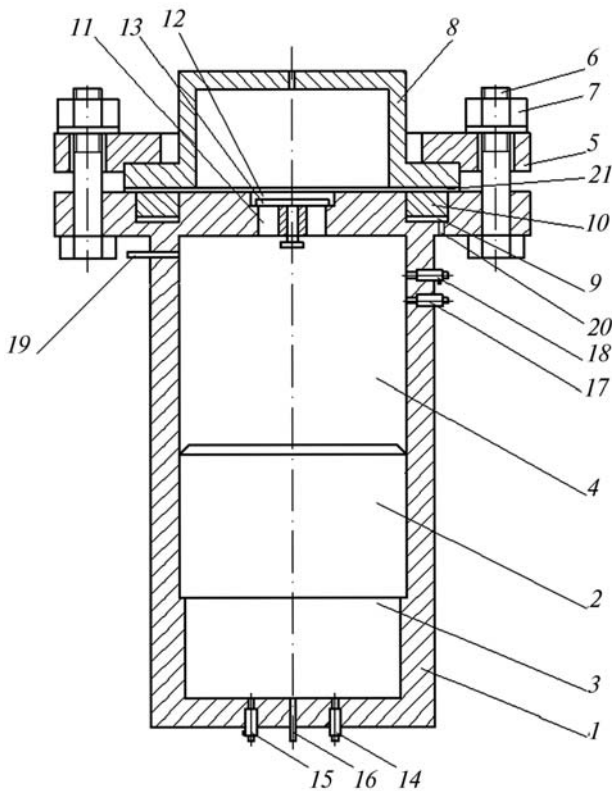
Схема двухкамерного устройства для газовой штамповки:
